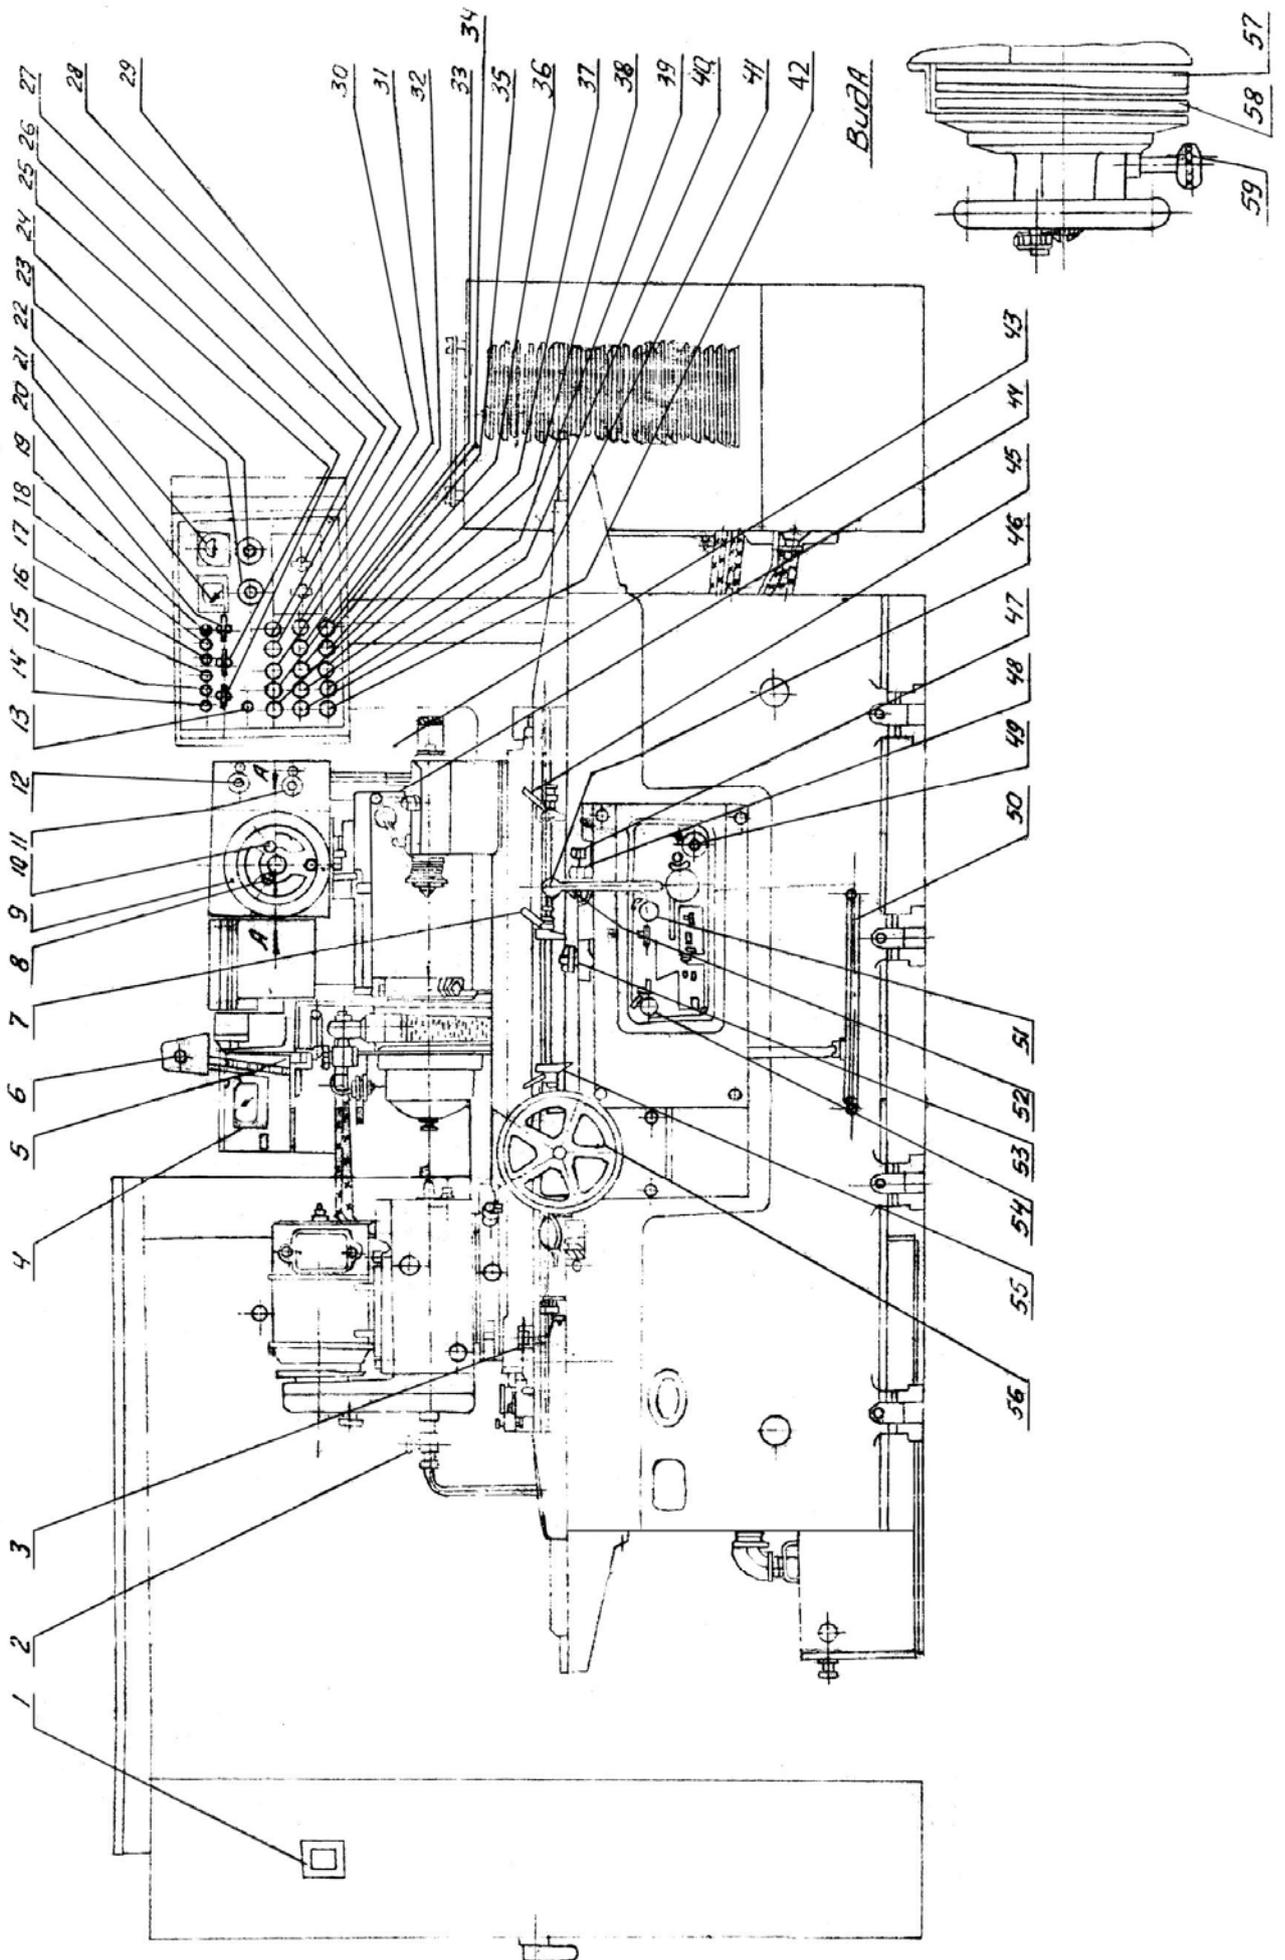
Общий вид станка с обозначением органов упр-я и контр. устройств.
